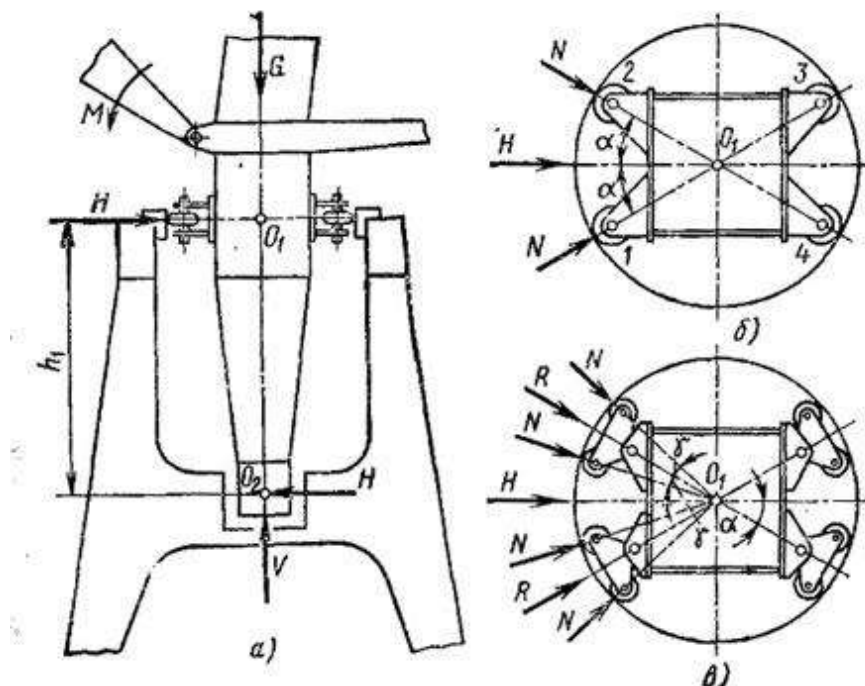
Опорно-поворотний пристрій на колоні (кран КППГ-5)
